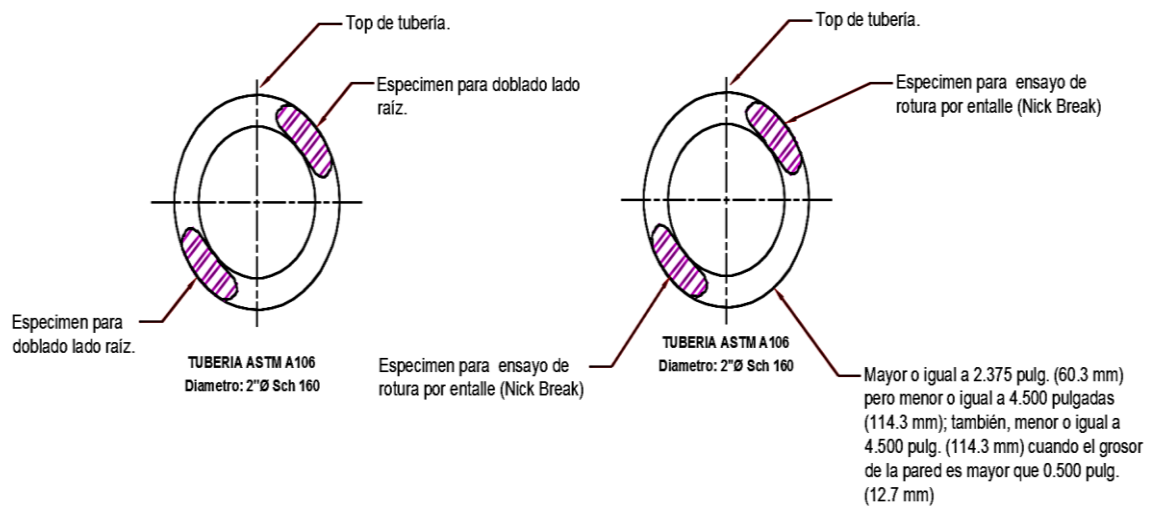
Locación de probetas de soldadura a tope para calificación de soldadores. Fuente: Figura 12 – API 1104
